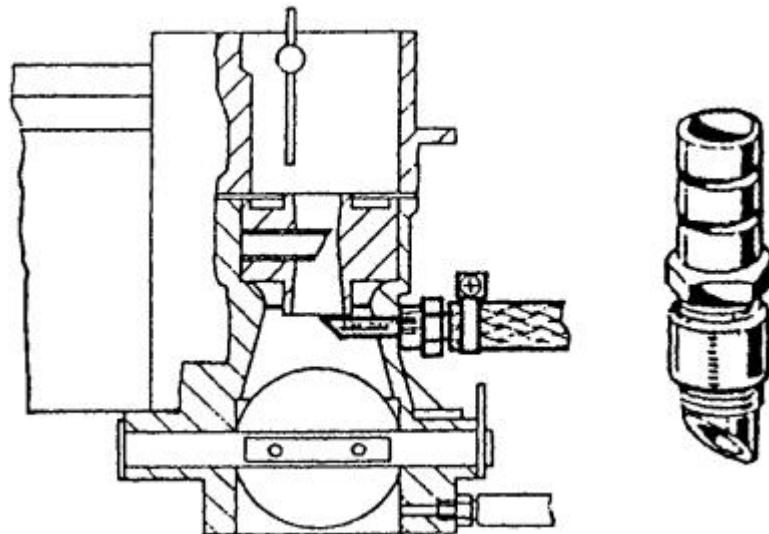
Газовый штуцер и его установка в карбюраторе.
